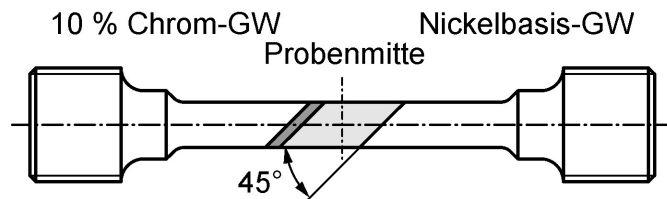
Schweißnaht unter 45° bei Probe 10 und Probe 11
